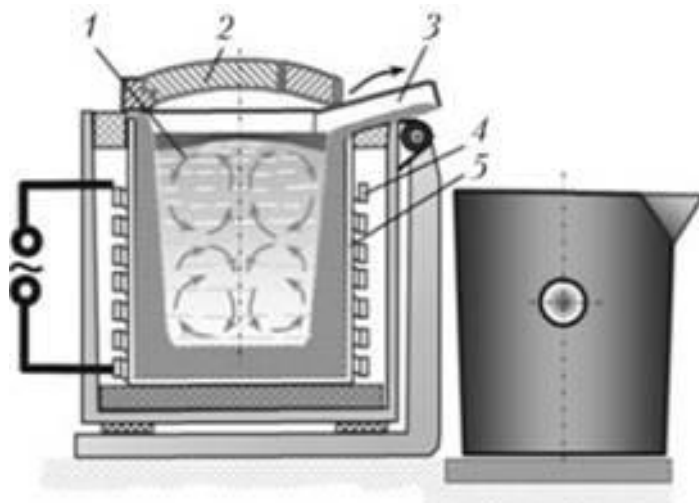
Індукційна тигельна плавильна піч: 1 - металева шихта - одержуваний чистий метал; 2 - знімне склепіння; 3 - зливний носок; 4 - індуктор; 5 - тигель
